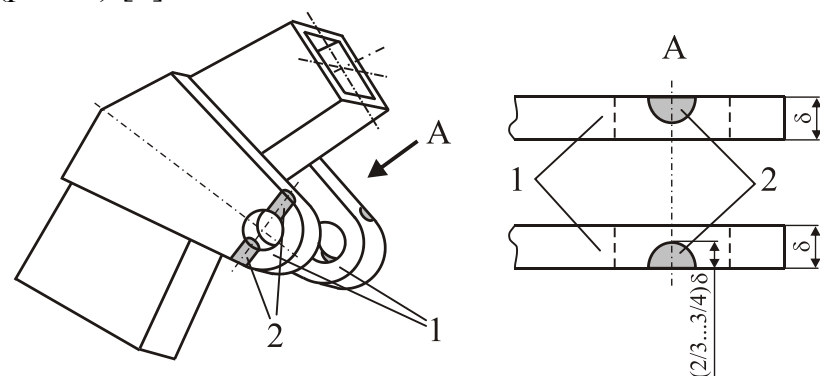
Схема упрочнения: 1 – проушины; 2 – наплавленный материал
